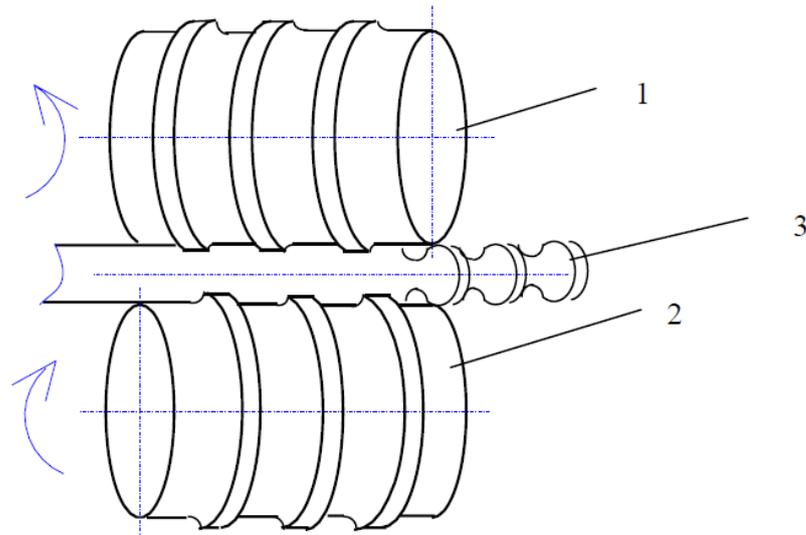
Поперечно-гвинтова прокатка в спіральних калібрах
